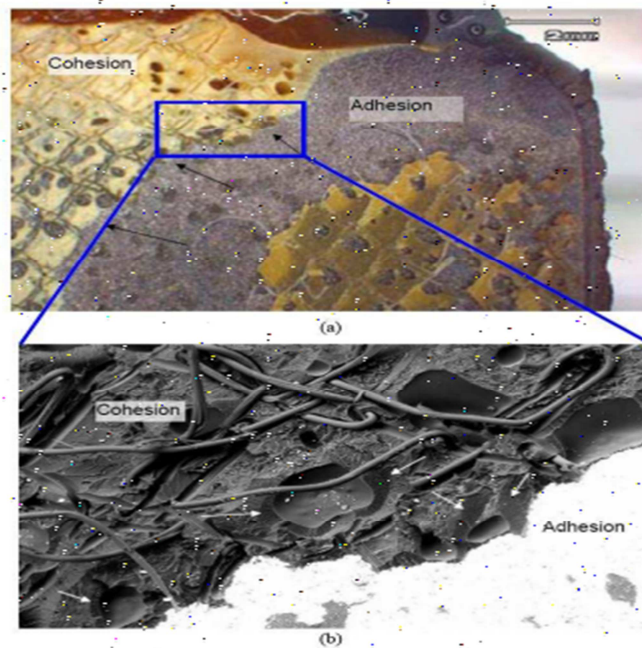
Observation d'une rupture mixte d'un joint collé par MEB [87]
